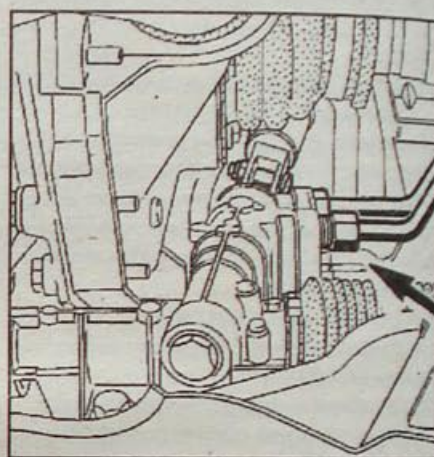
Место отсоединения шланга высокого давления усилителя рулевого управления от корпуса рулевого механизма
